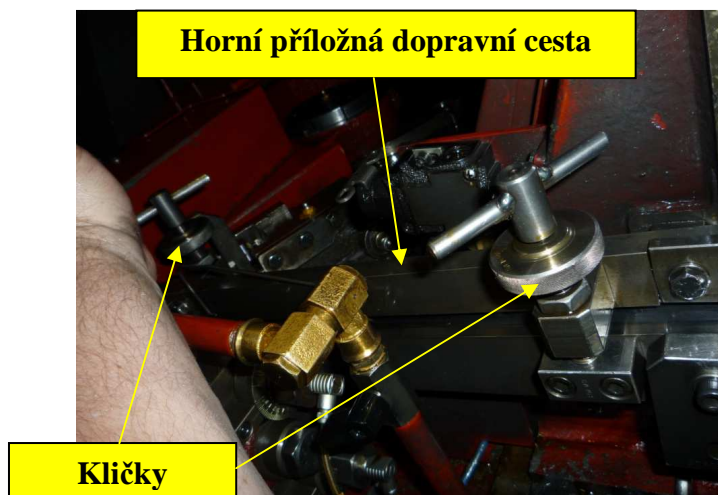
Demontáž horní příložné dopravní cesty do kupy
